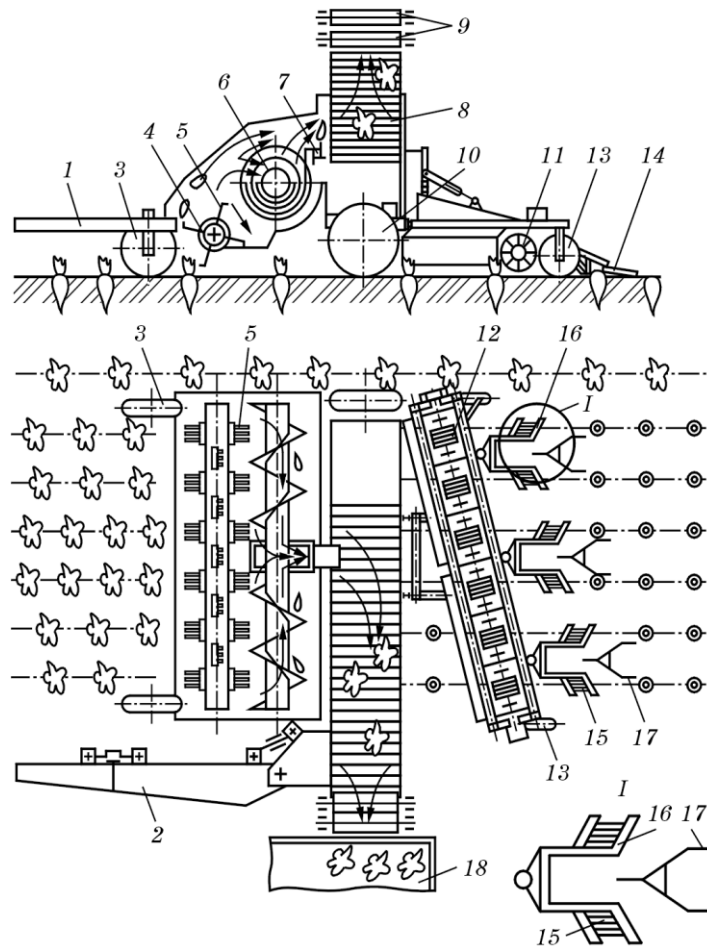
Конструктивно-технологічна схема гичкозбиральної машини МБП-6:1 – основна рама; 2 – причіпний пристрій; 3, 13 – копіювальне колесо; 4 – ротор; 5 – секція молоткових ножів; 6 – шнековий конвеєр; 7 – лопатевий бітер; 8 – вивантажувальний елеватор; 9 – бітер-метальник; 10 – опорне колесо; 11 – очисник головок коренеплодів; 12 – очисні елементи; 14 – обрізник головок; 15 – гребінчастий копір; 16 – пасивний ніж; 17 – пасивний копір-водій; 18 – кузов транспортного засобу
